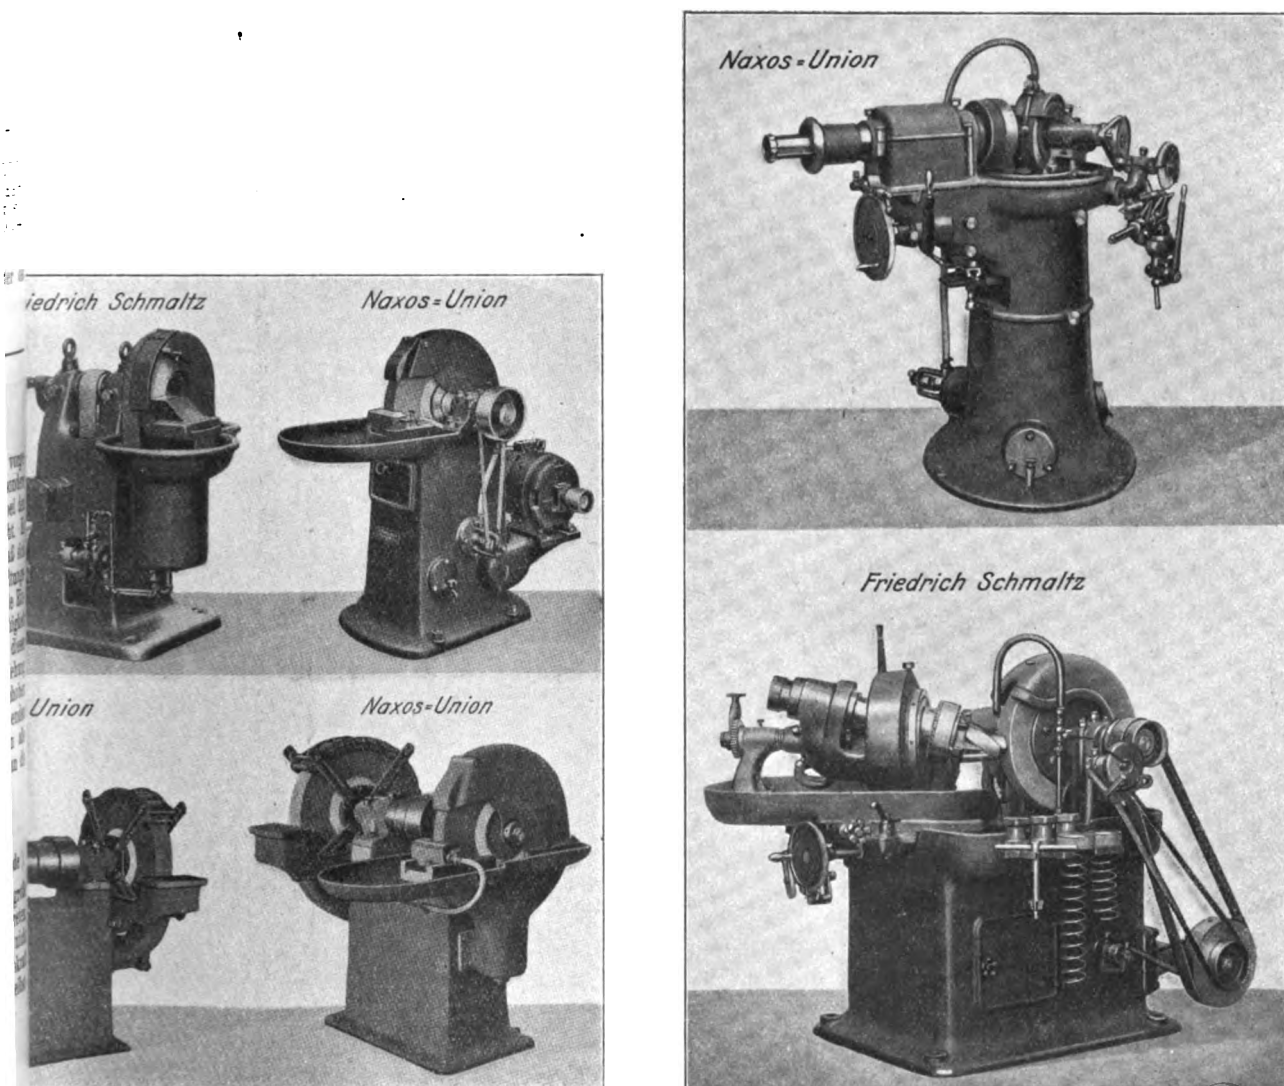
Selbsttätige Spiralbohrer-Schleifmaschinen.
